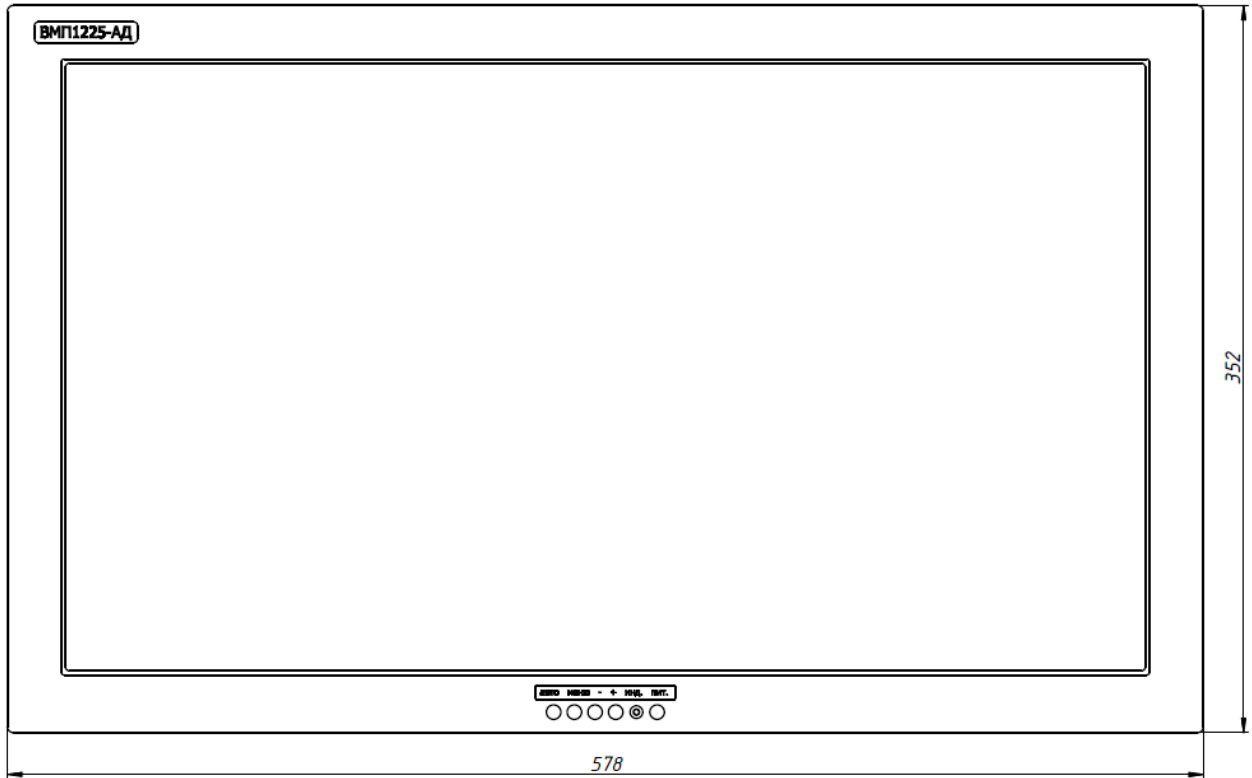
Габаритный чертёж лицевой части видеомонитора
